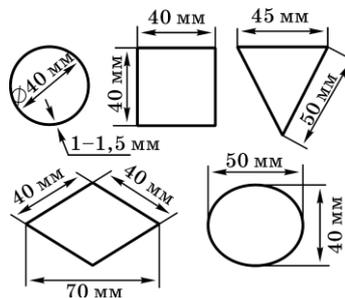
Формы и размеры клейм для товароведческой маркировки мяса
